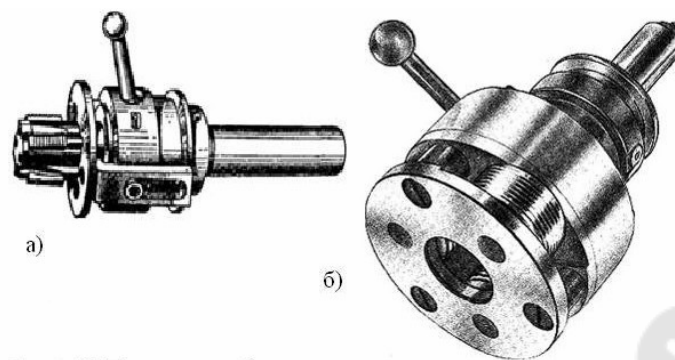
Головки резьбонакатные: а – для внутренней резьбы; б – для наружной резьбы
